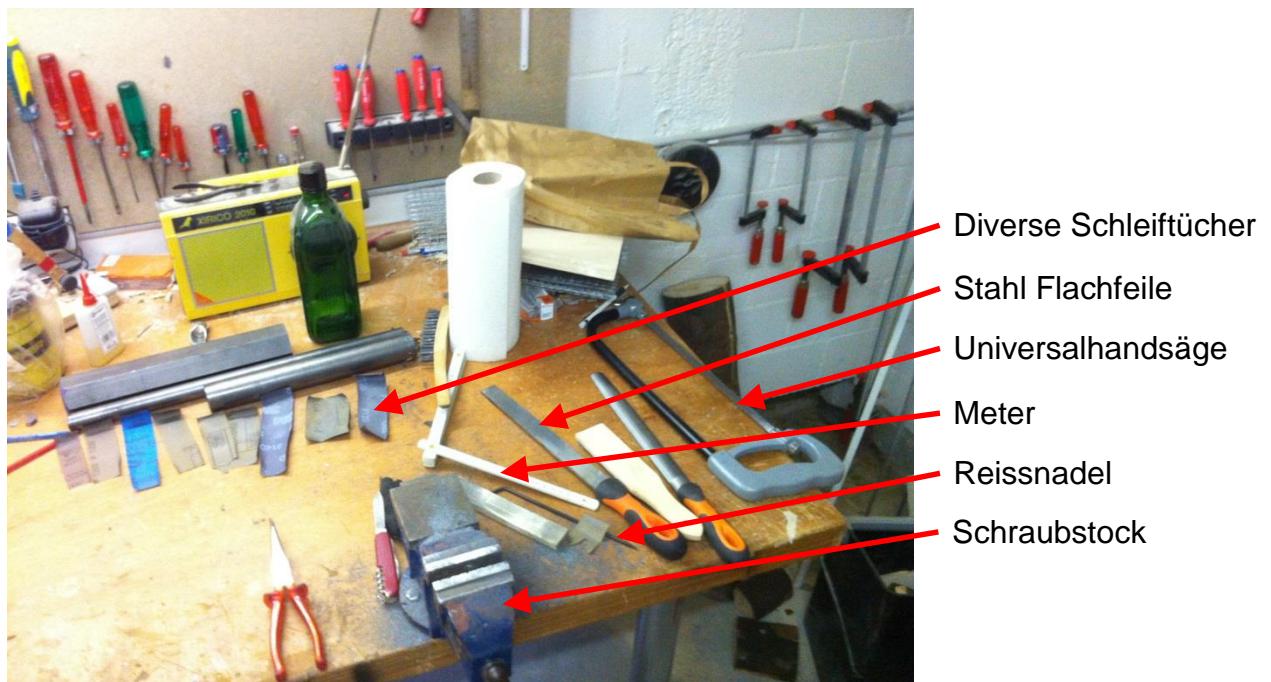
Benutzte Werkzeuge für die Bearbeitungen der Proben.
